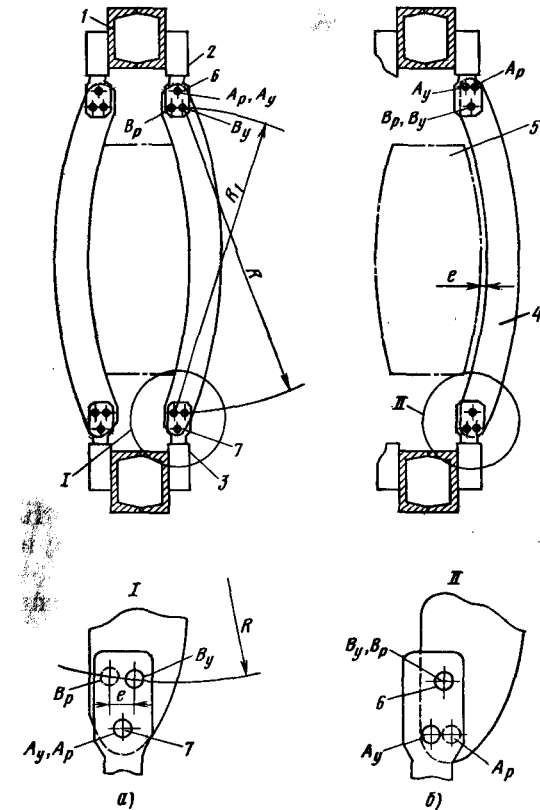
Приспособление для сборки и контроля агрегата:
